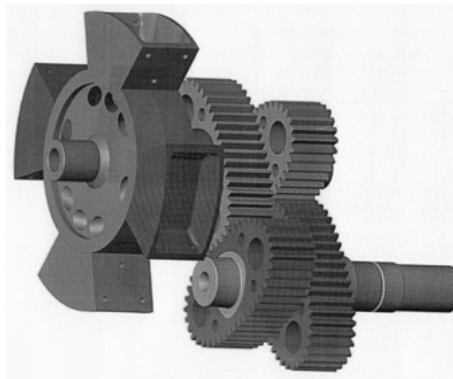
«Вращающийся» вариант роторно-лопастного компрессора
